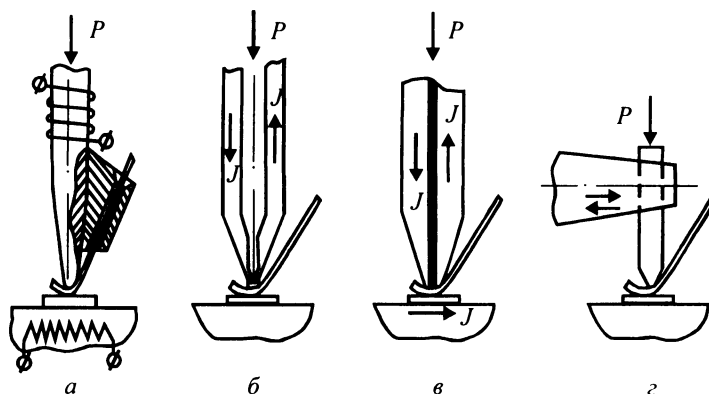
Виды микросварки и разновидности сварочного инструмента:
